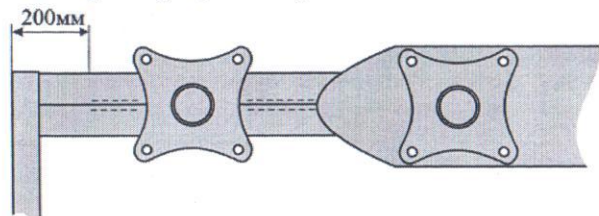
Контроль околошовной зоны сварного соединения на нижней стенке продольных балок рамы
